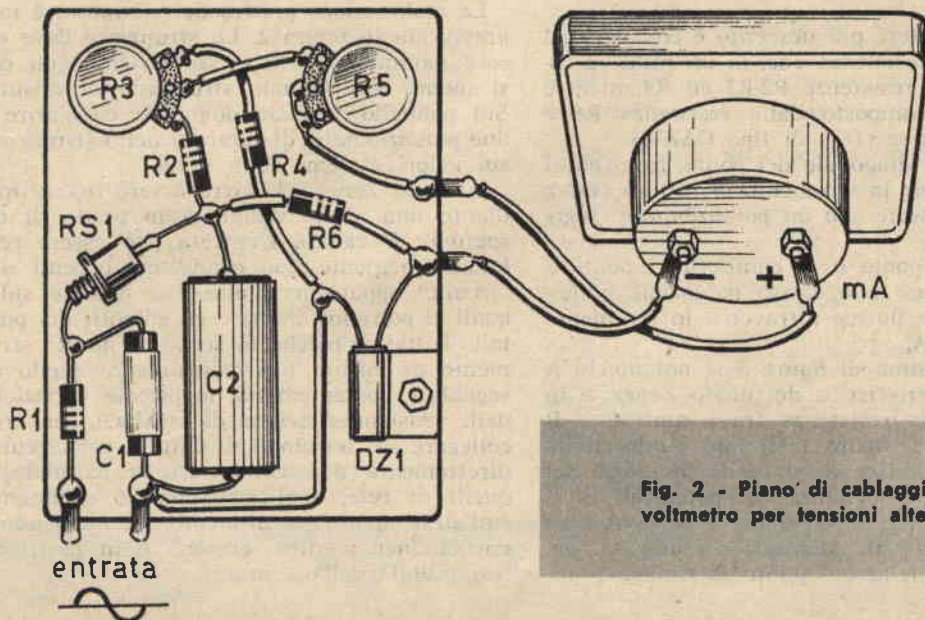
Piano di cablaggio del voltmetro per tensioni alternate.
